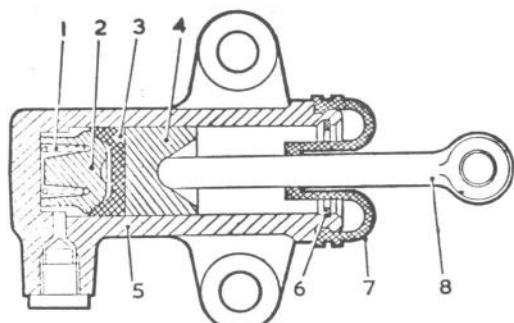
Sección en el cilindro receptor de mando del embrague.
